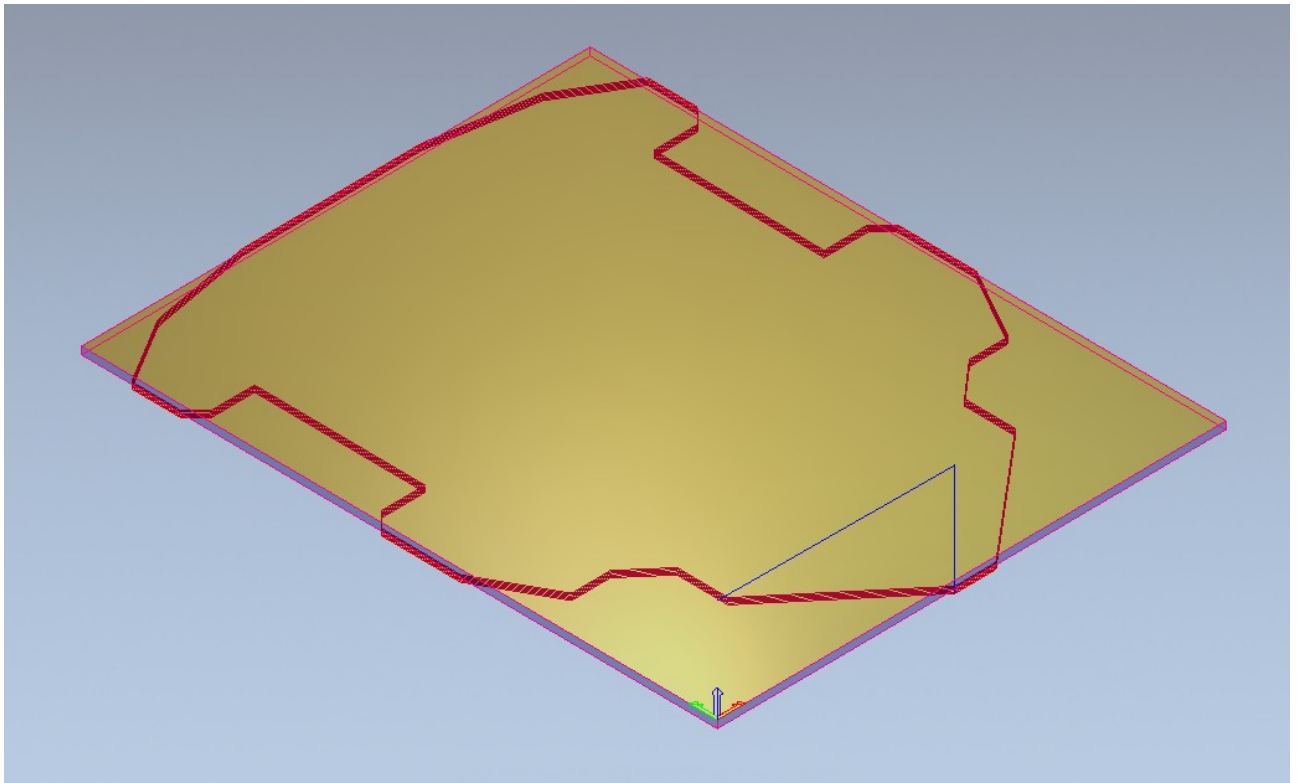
Траекторія руху інструмента на фрезерування контуру
